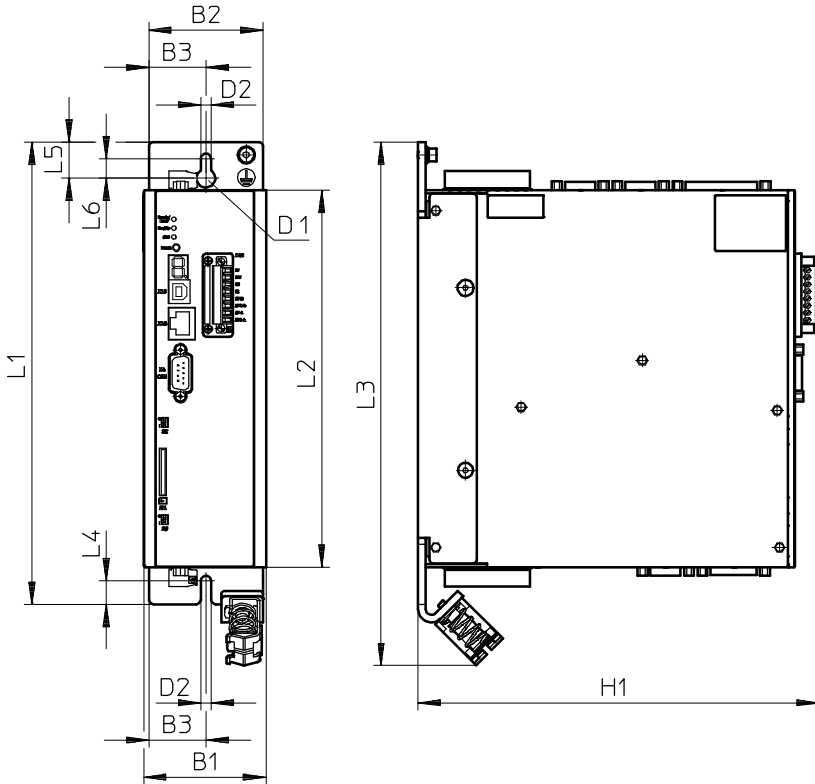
Controlador de motor CMMP-AS-...-M0: Placa de montaje
